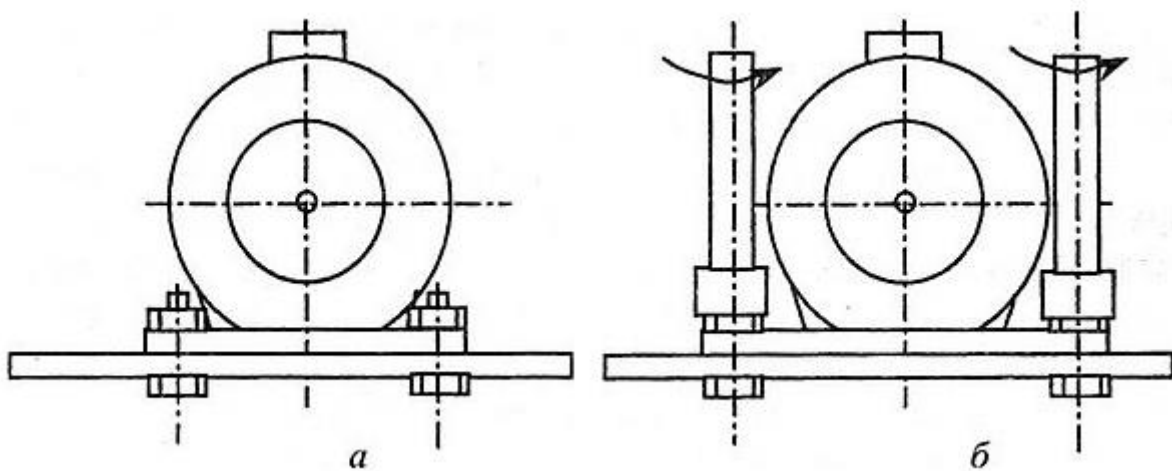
Изменения конструкции изделия для обеспечения подвода автоматических гайковертов
